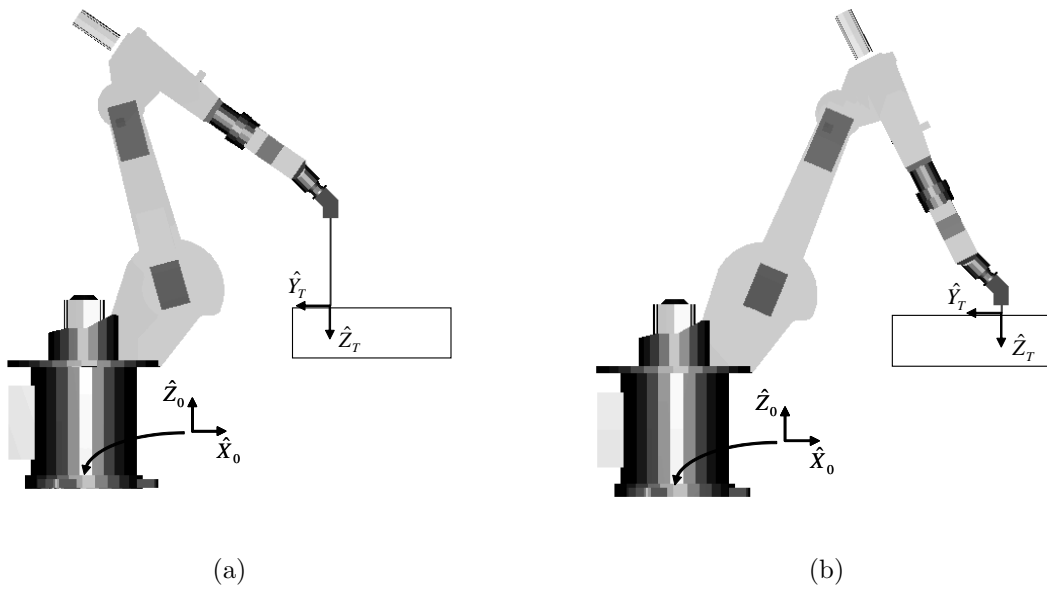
Posições inicial (a) e final (b) do manipulador durante a soldagem com eletrodo revestido para soldagem com ângulo de  $90^\circ$ .
